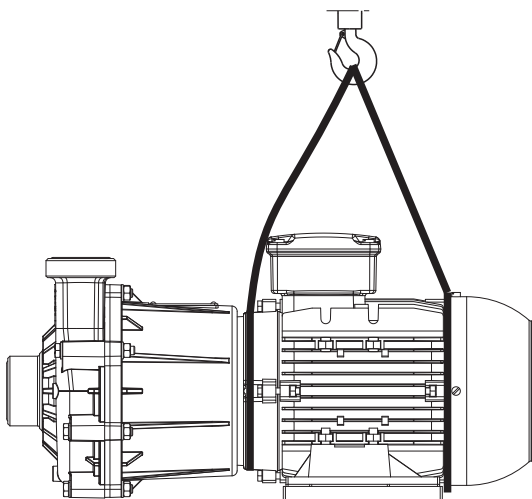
Hebezeug an der Blockpumpe befestigen (Prinzipbild)
